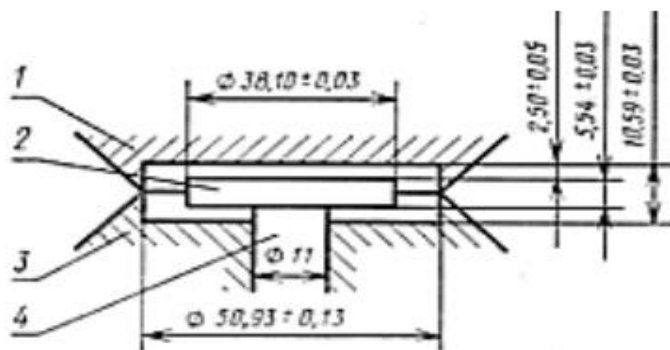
Испытательная камера: 1 – верхняя цилиндрическая полуформа; 2 – дисковая головка ротора; 3 – нижняя цилиндрическая полуформа; 4 – стержень ротора
